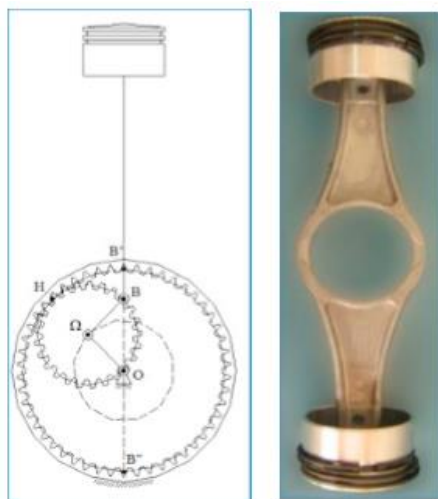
прототип поршневого компрессора, на основе планетарной передачи.
